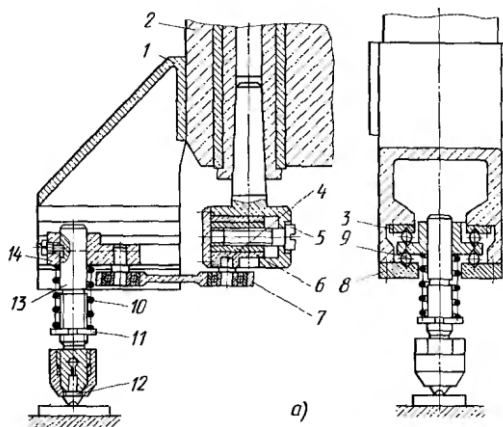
Конструкція віброголовки для обробки плоских поверхонь
